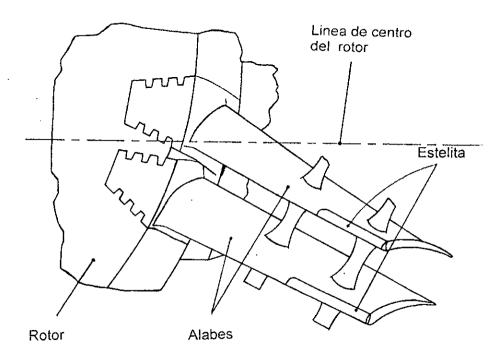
Posicion de los alabes para la soldadura de la etelita.
